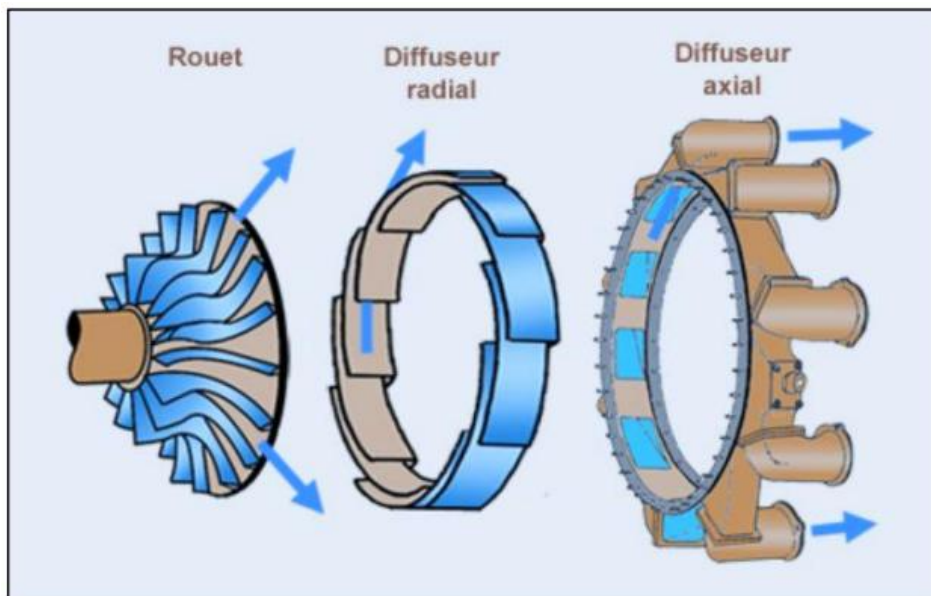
Dessin des constituants d'un compresseur centrifuge
